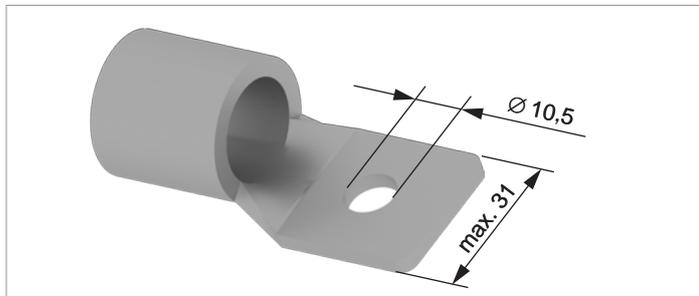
Zulässige Abmessungen der Kabelschuhe
